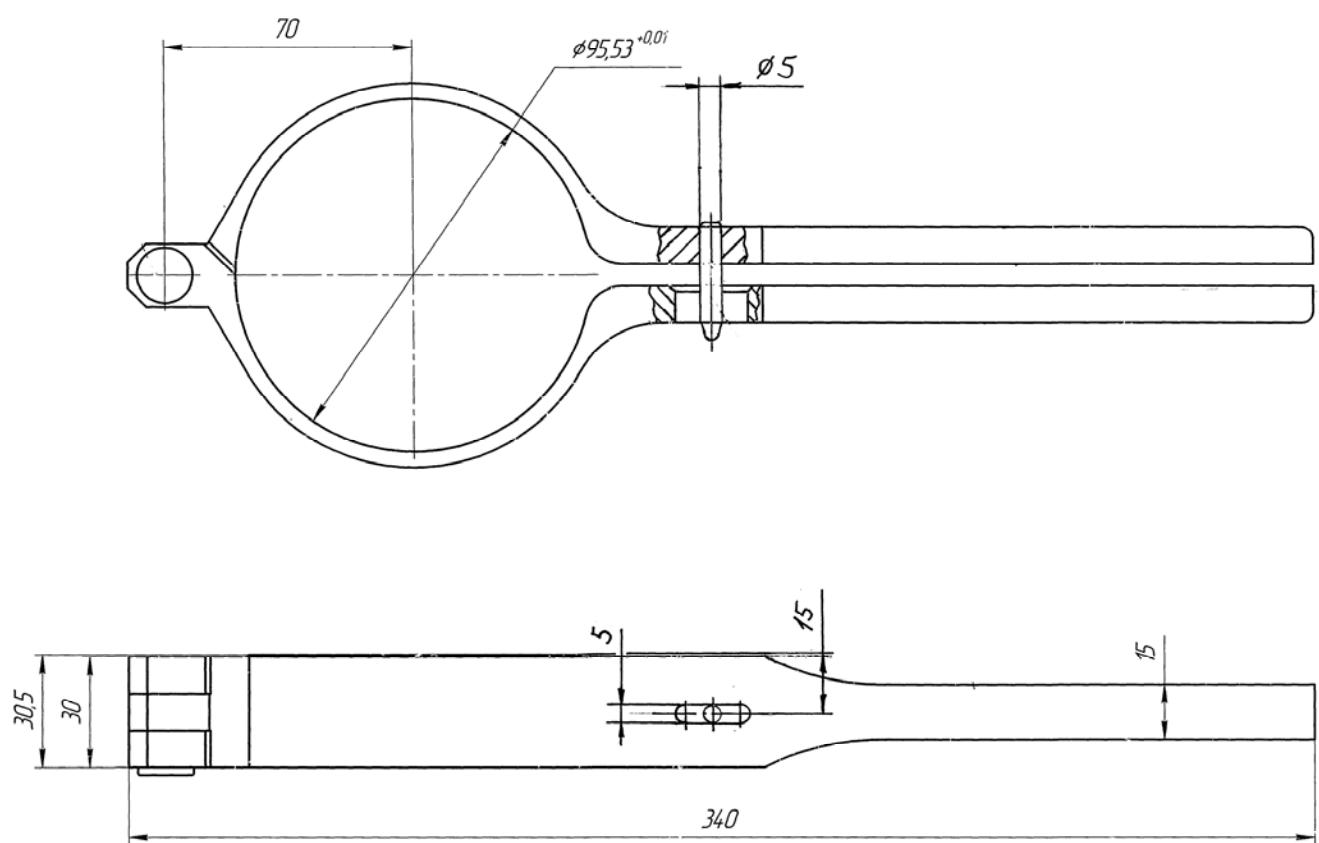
ЗМ 7820-4517, Оправка для сжатия поршневых колец \varnothing 95,5 мм
